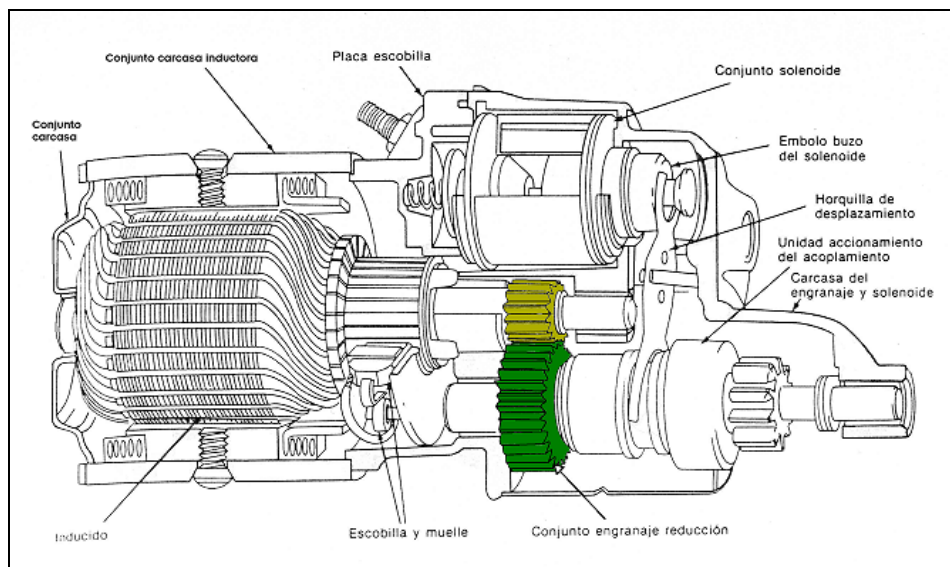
Motor de arranque con engranaje de reducción y acoplamiento de rueda libre.
